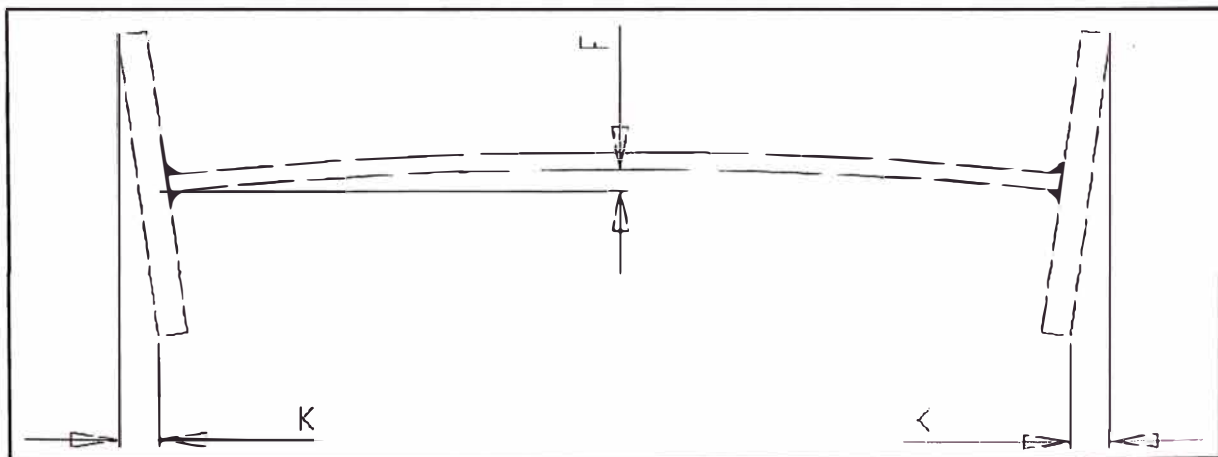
Secciones soldadas, rectitud y paralelismo
